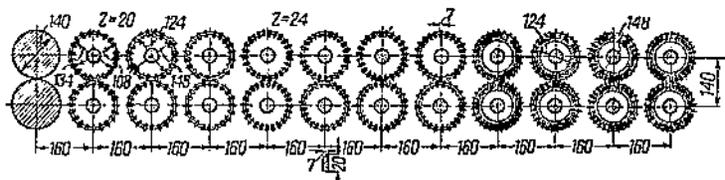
Схематический разрез ножевой мялки для льна завода Фрембса и Фреуденберга
